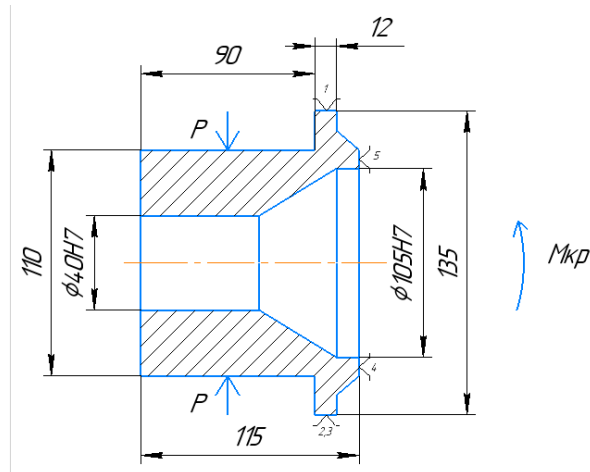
Розрахункова схема для визначення сил і моментів, що діють на заготовку при свердлінні
